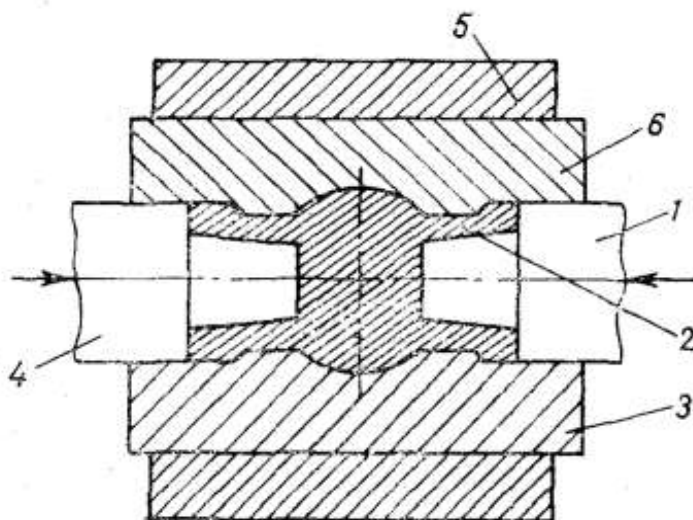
Штампування поковок прошиванням у рознімній матриці: 1, 4 – пуансони; 2 – поковка; 3, 6 – частини рознімної матриці; 5 – обойма
